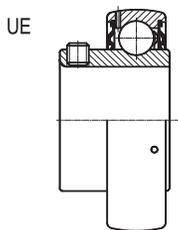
Регулируемые шариковые подшипники с винтами - тип UE
